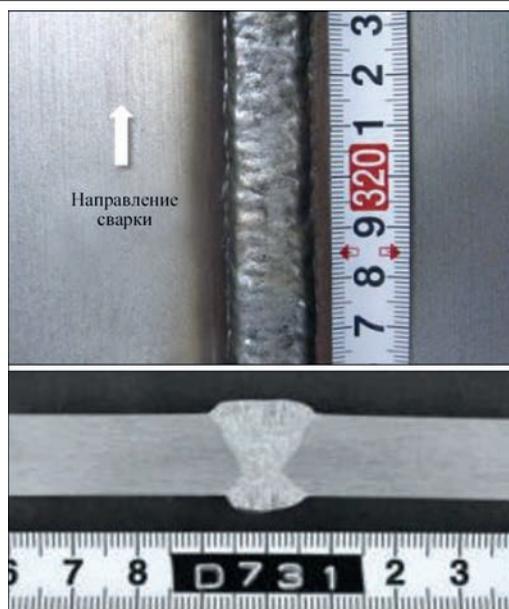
Внешний вид валика сварного шва и макроструктура стыкового соединения DW-2594 (3G)
